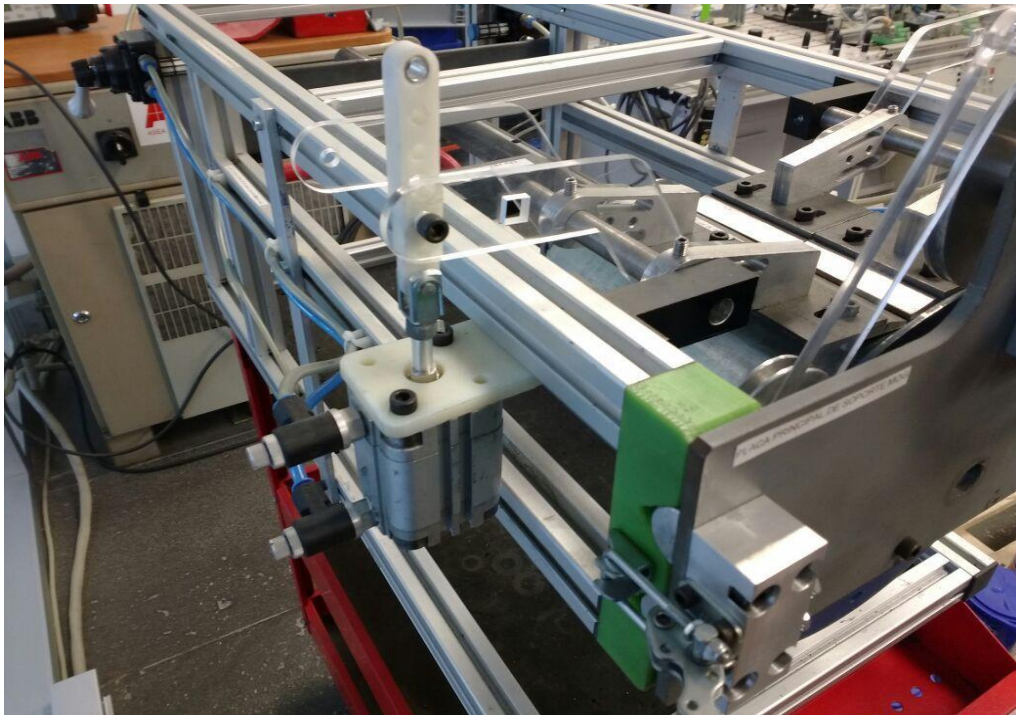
Se muestra el prototipo físico ensamblado del sistema para soldadura lineal y orbital
